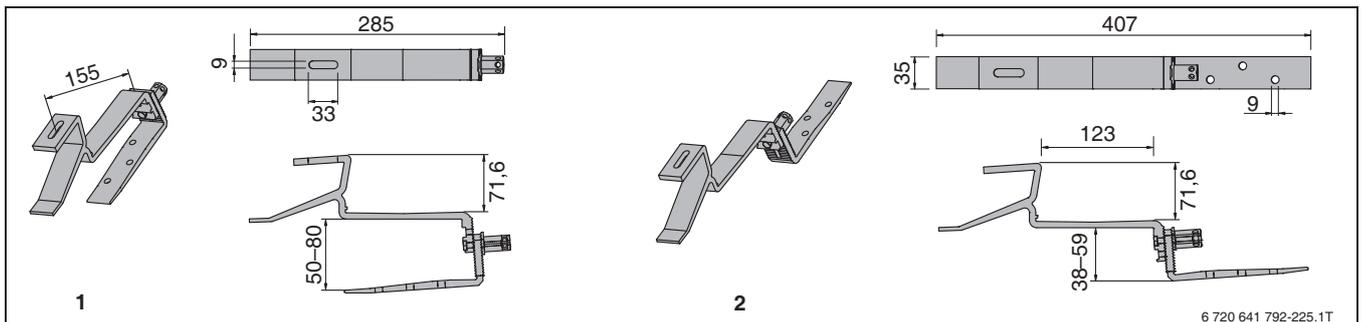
Collegamento da tetto per coperture con tegole, tegole in laterizio e embrici CKN1.0 e SKS4.0 (misure in mm)
